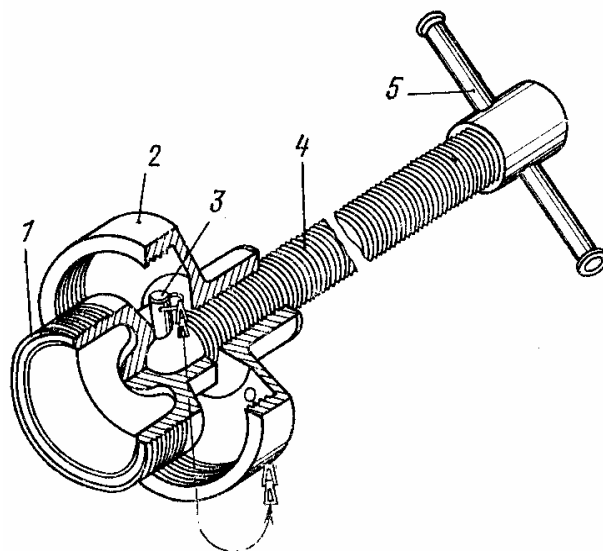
Приспособление 154.80.9942.010 для съема колес передней ноги шасси:
